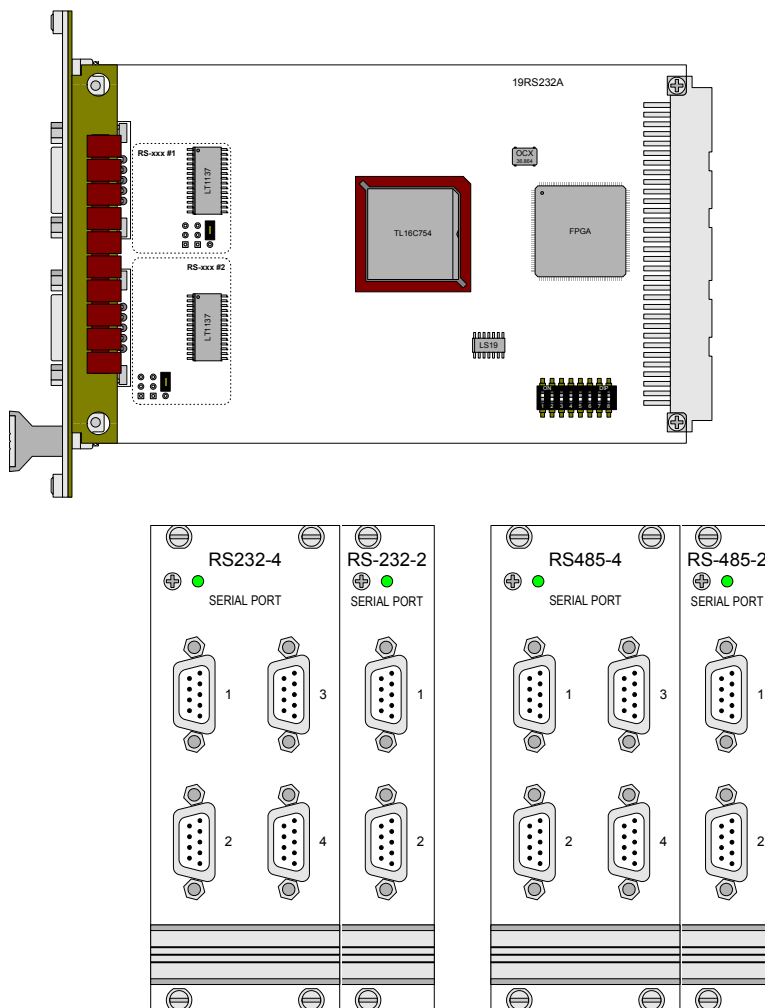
Pro-RSxxx: Platine und Frontplatten
